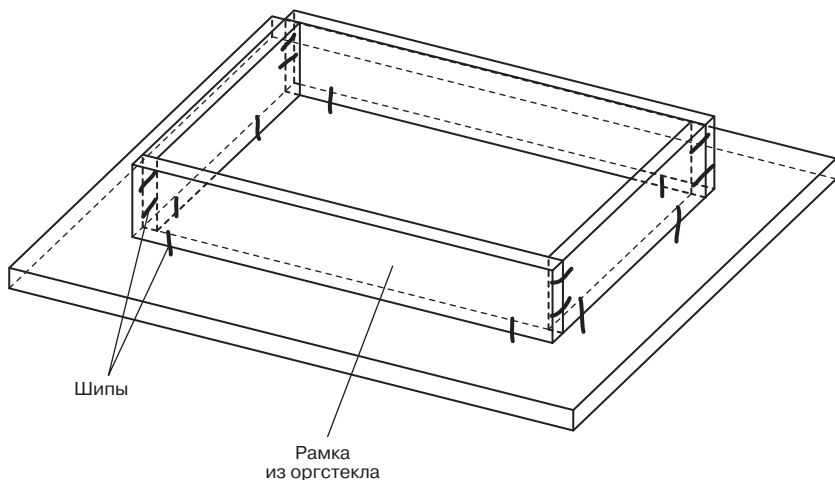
Технология изготовления корпуса из эпоксидной смолы
